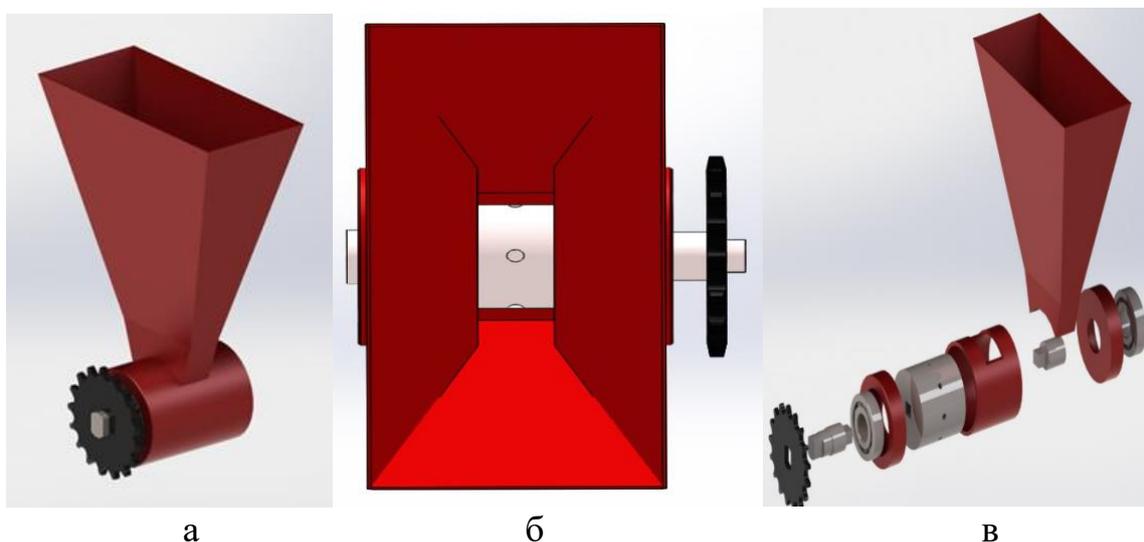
Высеваящий аппарат: а – вид общий; б – вид сверху; в – в разборе
